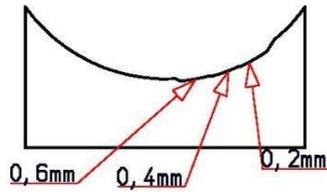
Les profondeurs de coupe sur la jauge à couteaux
